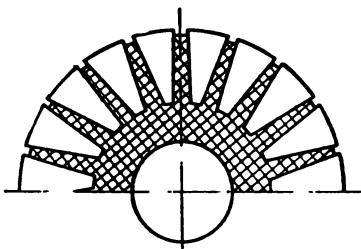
Коллектор с прессованной заготовкой пластин.
